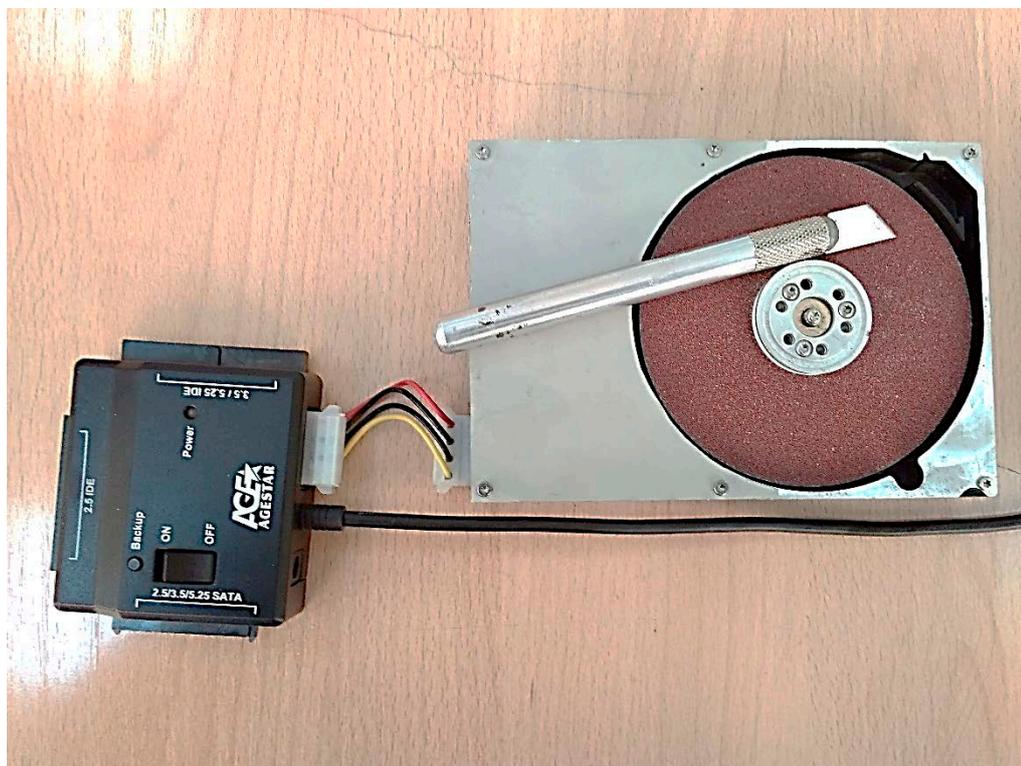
Полировально-шлифовально-заточный мини станок
